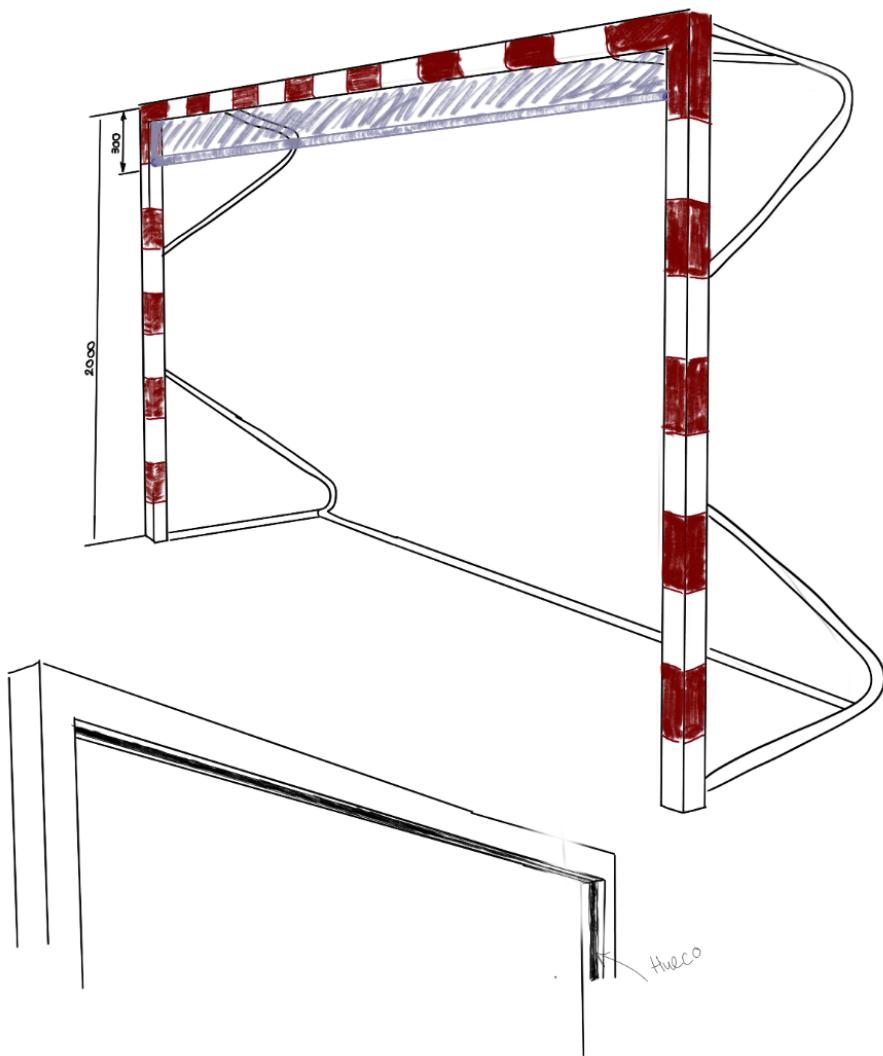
Boceto portería adaptable con el toldo integrado y detalle de la guía
